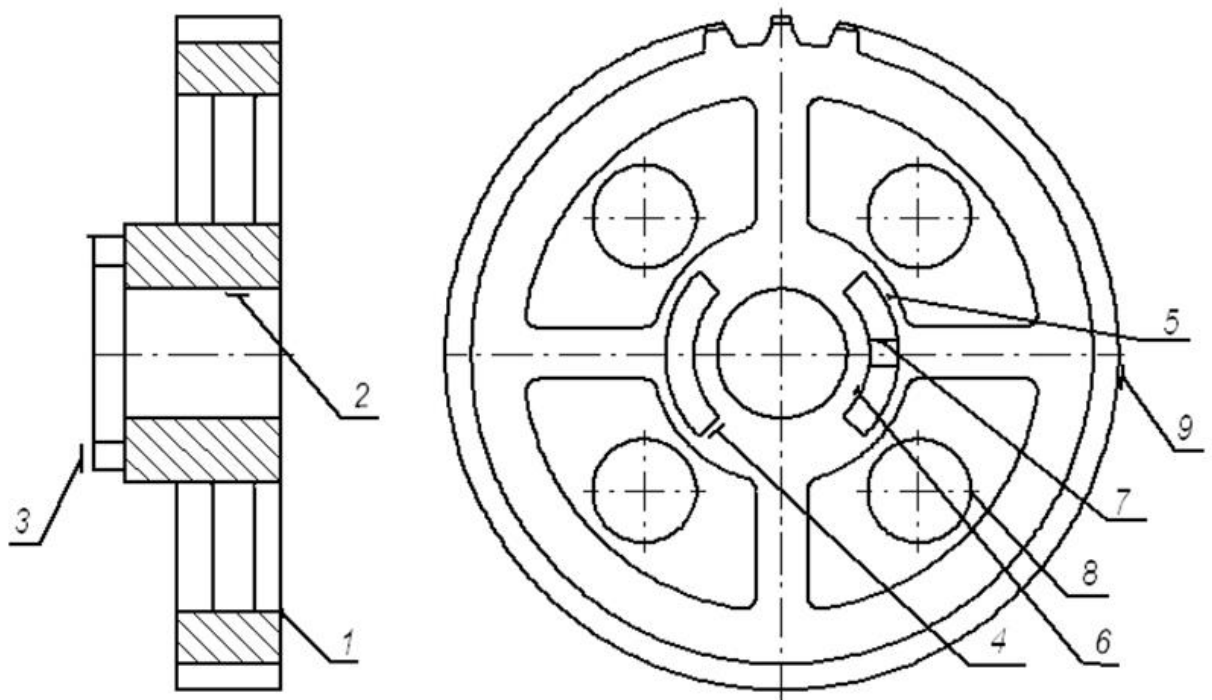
Оброблювані поверхні зубчатки СУЛ 103В
